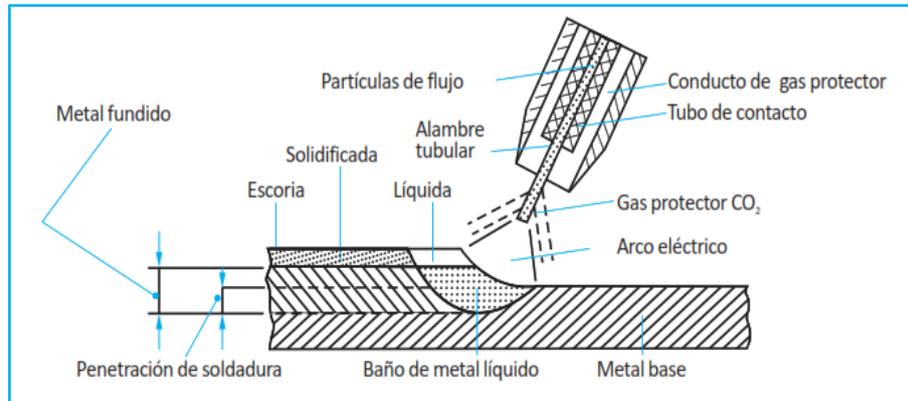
Soldadura por Arco Eléctrico con Alambre Tubular (FCAW)
